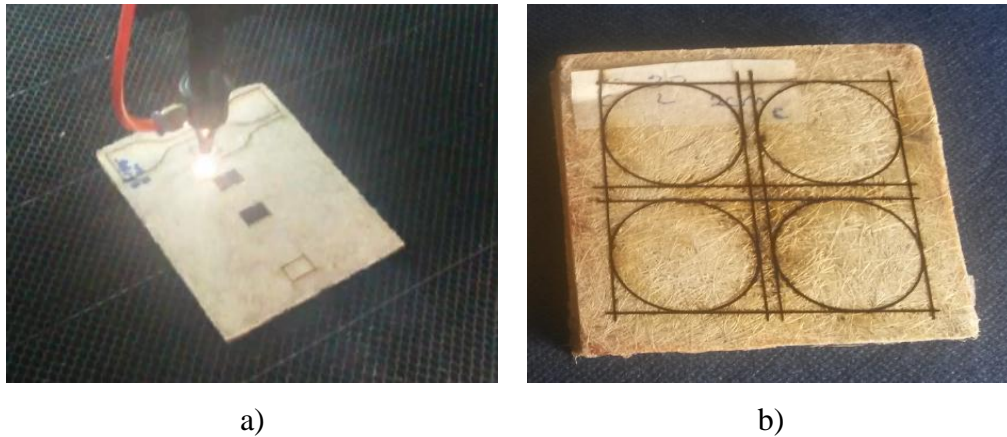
Corte de las probetas: a) probetas a tracción, b) Probetas a compresión
